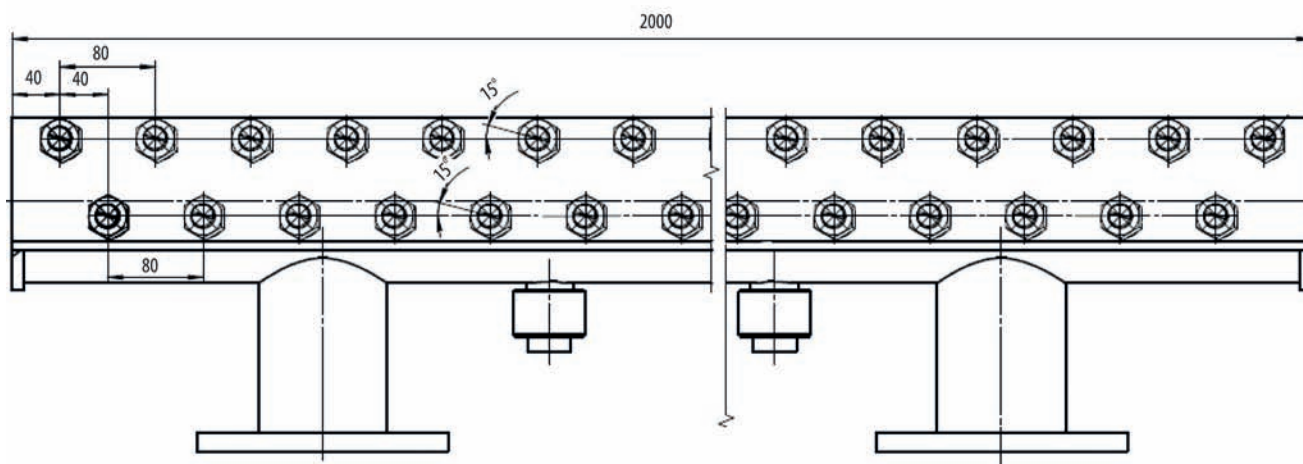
Схема коллектора охлаждения рабочих валков черновой группы стана 2000
